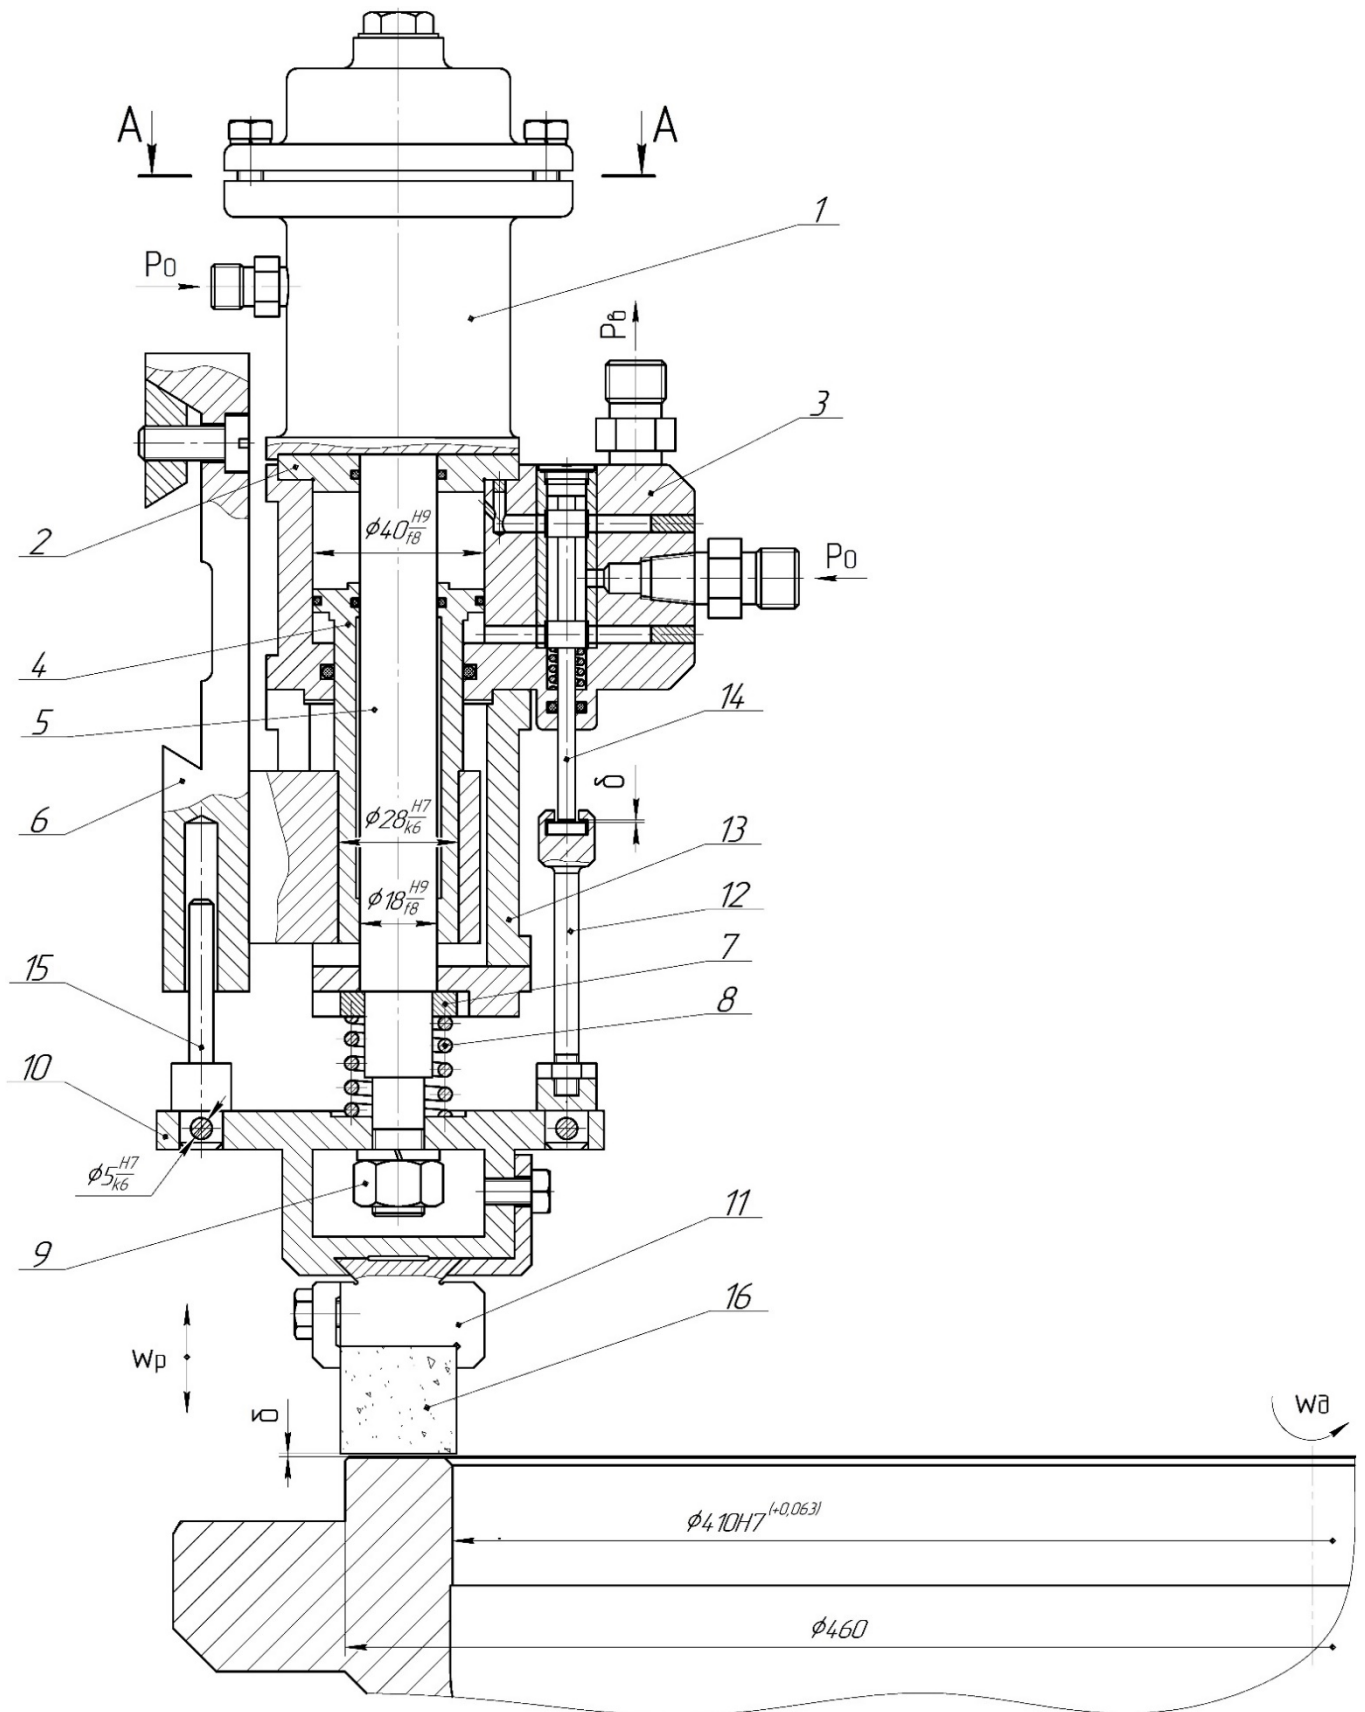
Пристрій для обробки площини заготовки способом подвійної осциляції брусків
